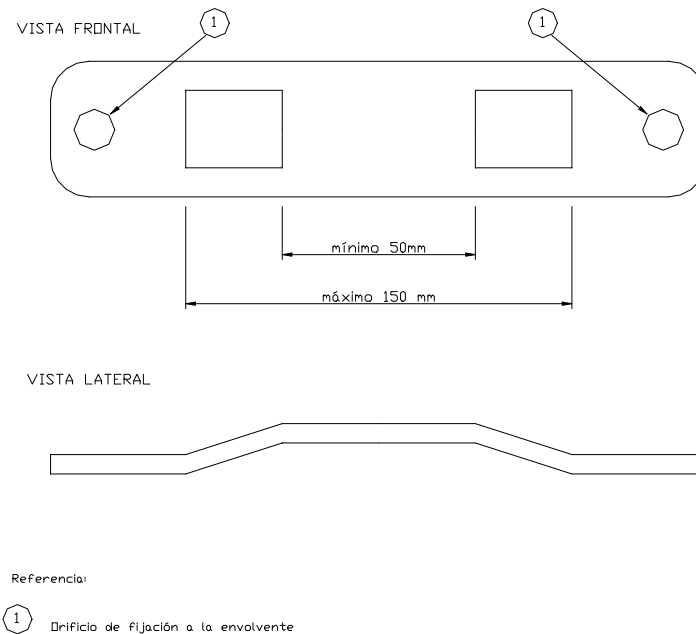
Esquema dispositivo de fijación de cajas en columnas
